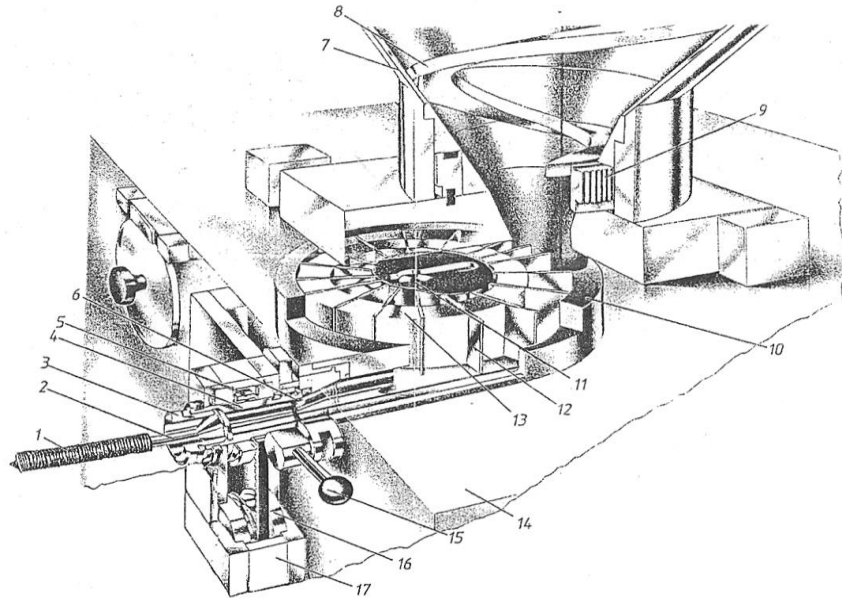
Принципова схема шприца з ексцентриково-лопатевим витиснювачем і механізмом перекручування фірми "Альпіна":
